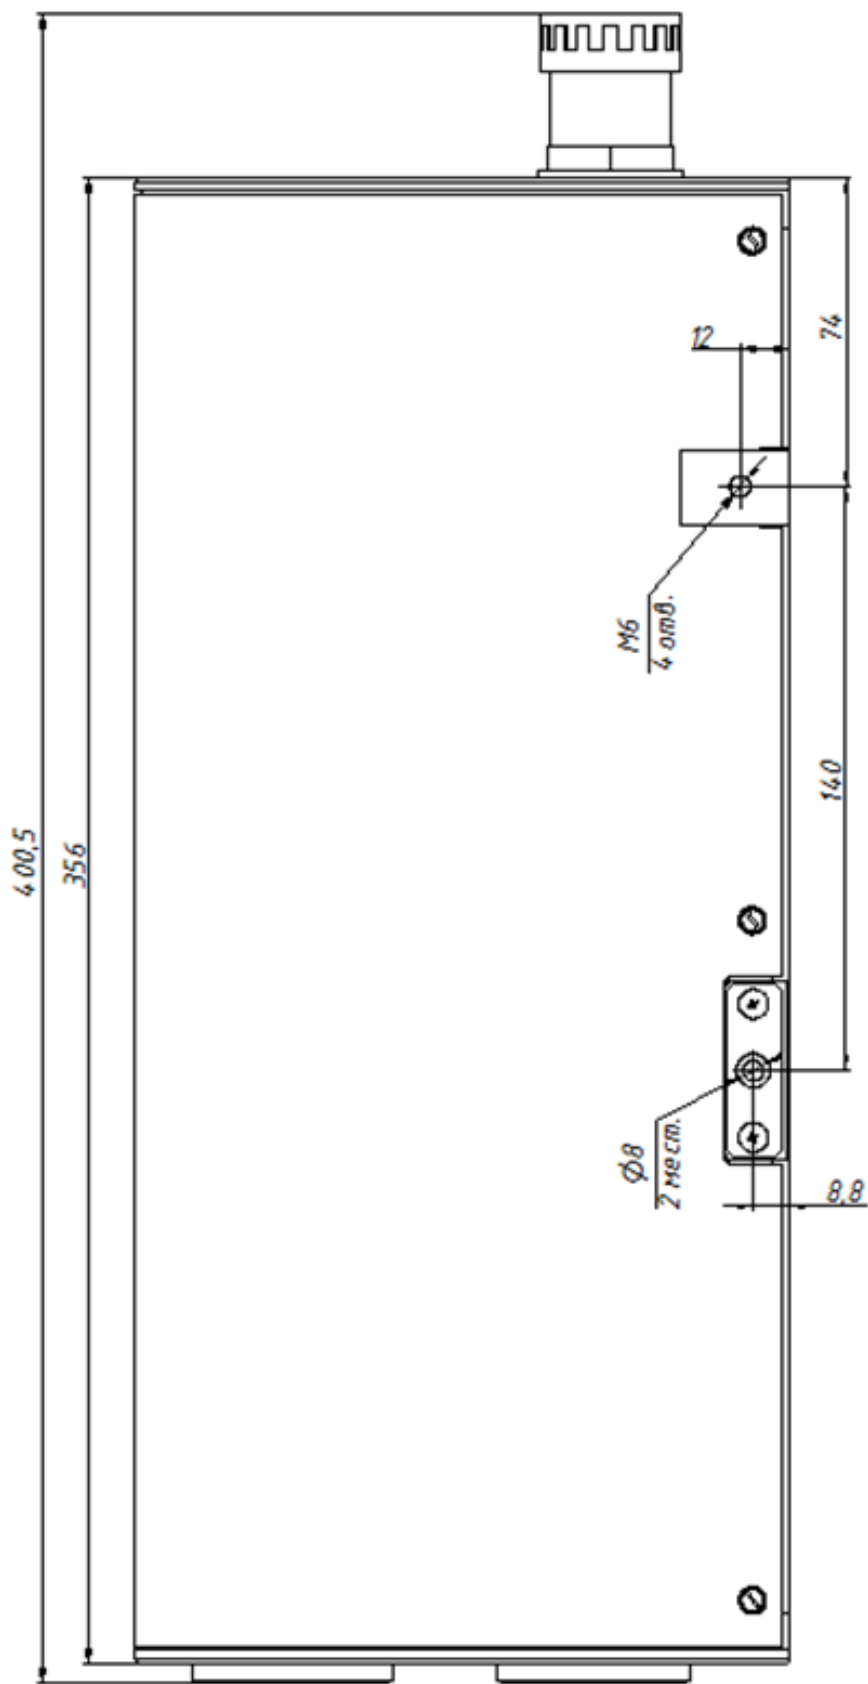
Габаритные размеры МЛИСФ-1 с боковой стороны
